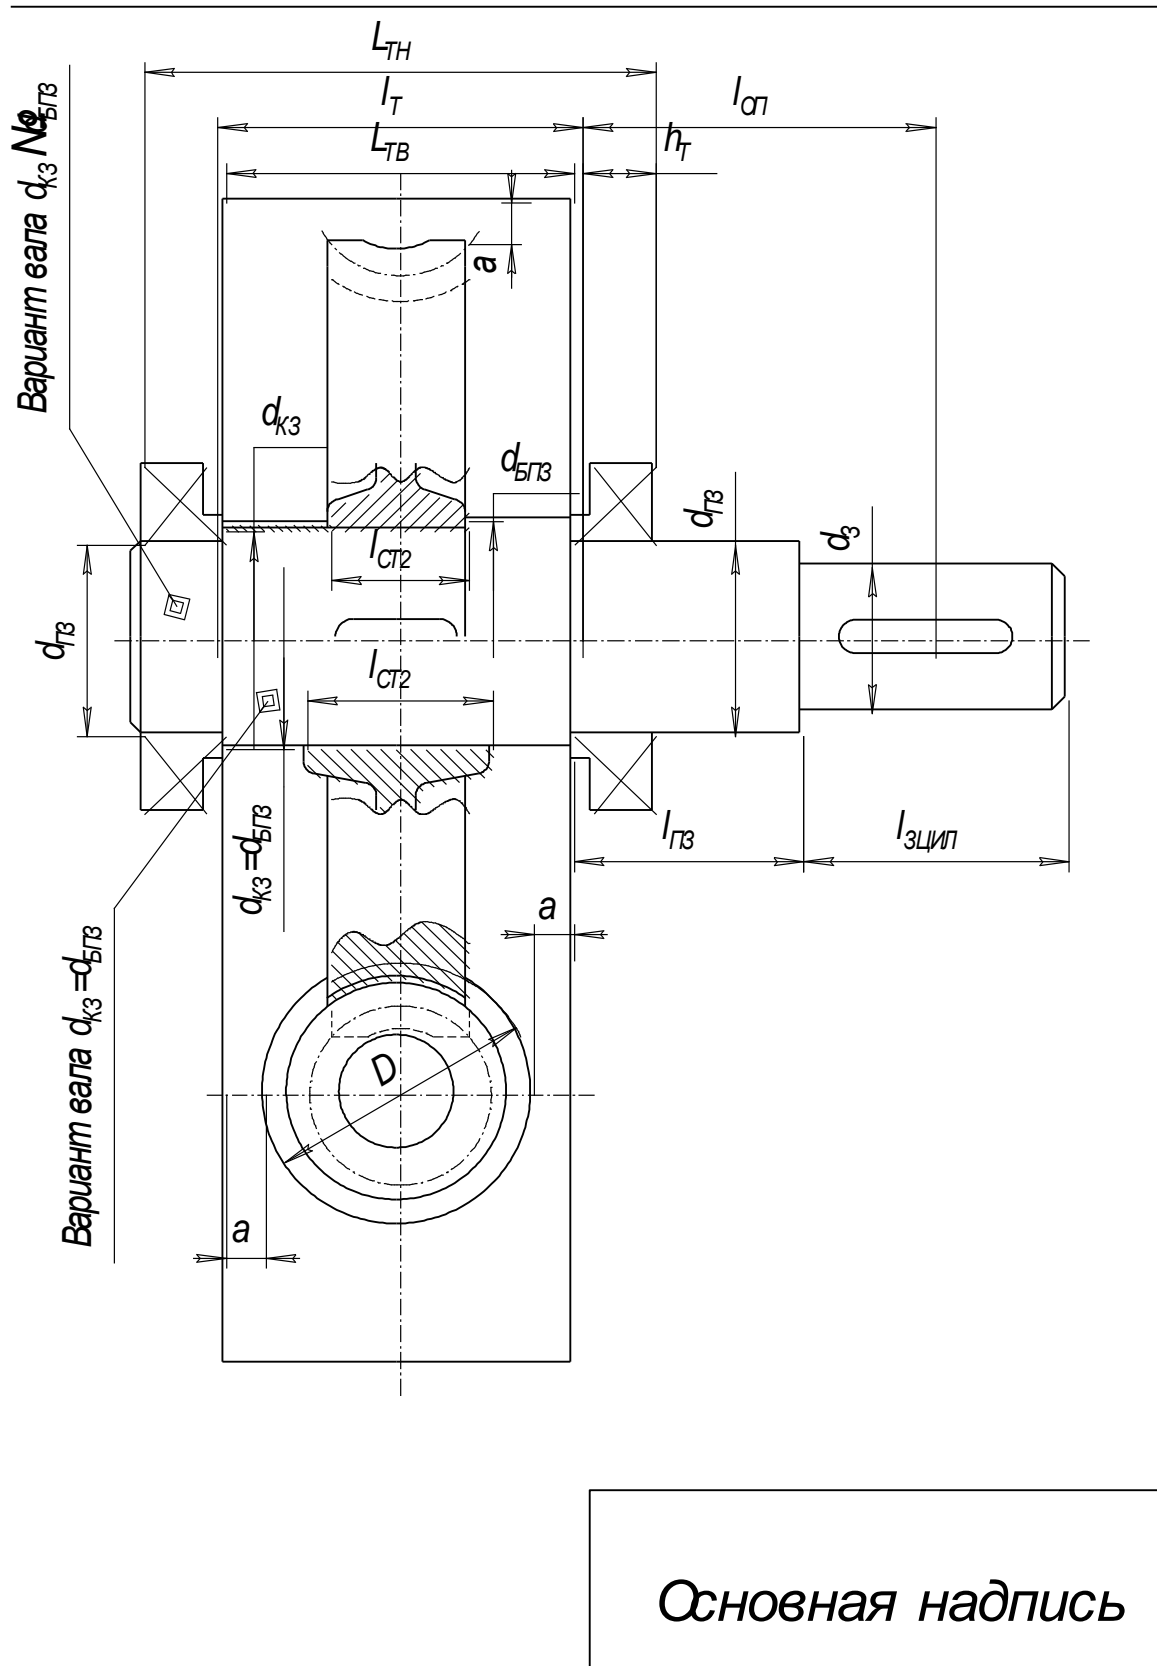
Пример эскизной компоновки червячного одноступенчатого редуктора
